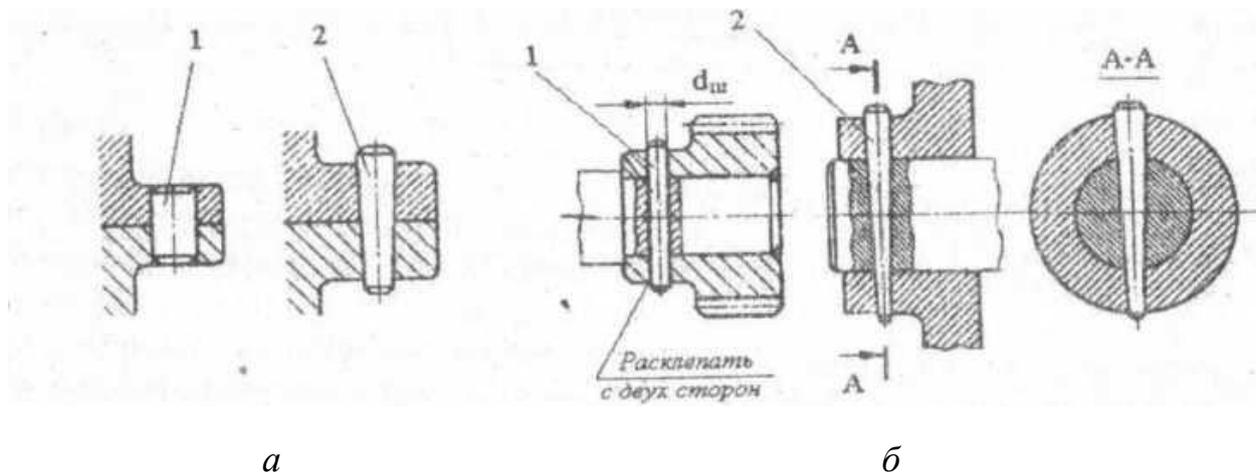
Штифтовые соединения деталей: *а* – для фиксации взаимного положения деталей; *б* – для передачи вращающего момента: 1 – штифт цилиндрический; 2 – штифт конический
